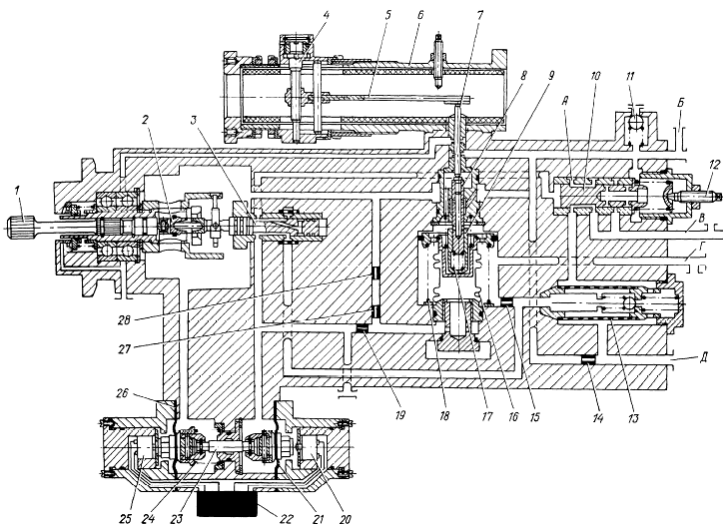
Командный агрегат КА-40 (конструктивная схема)
